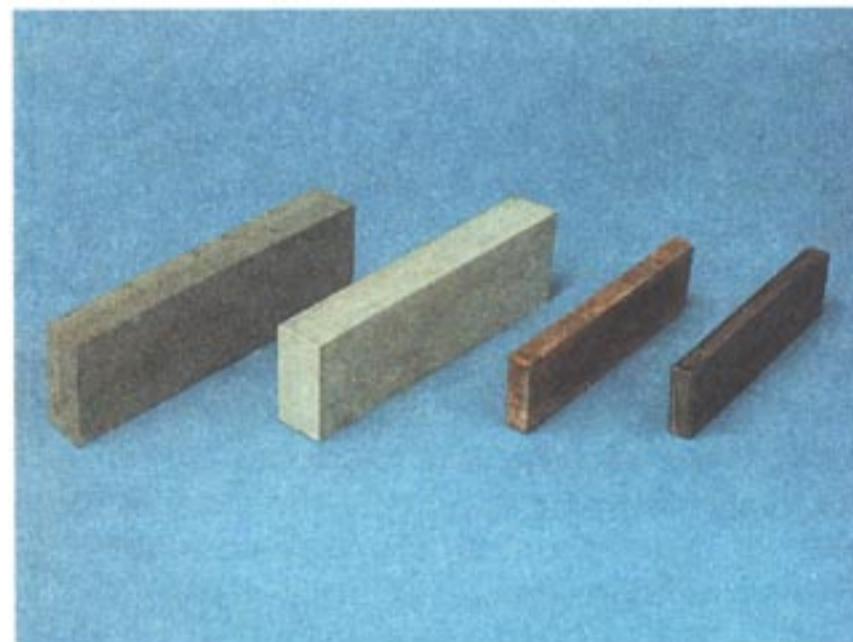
Бруски (слева направо): двухсторонний абразивный; доводочный мягкий; доводочный твердый; двухсторонний алмазный
